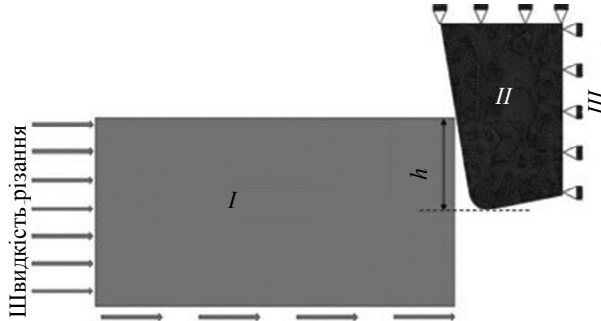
Вихідна скінченно-елементна модель процесу різання: *I* – заготовка; *II* – інструмент; *III* – нерухома опора; *h* – глибина різання.
